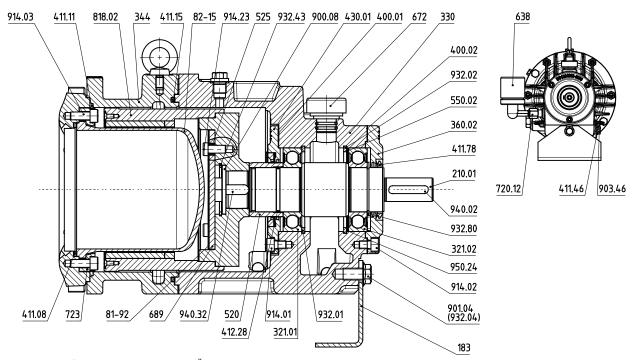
Ausführung Lagerträger mit Ölschmierung und Wellendichtring als Leckagebarriere
